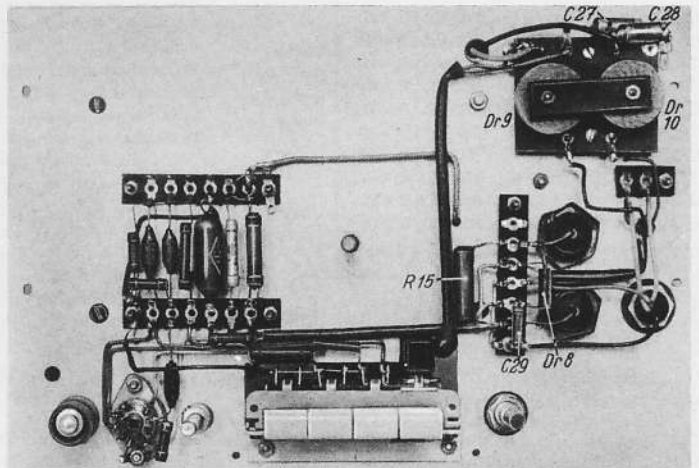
Hauptmontageplatte A, montiert und verdrahtet
